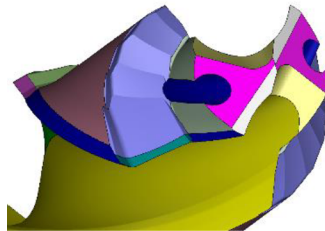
Detail geometrie díry zamýšlené k vyvrtání sruženým nástrojem.
